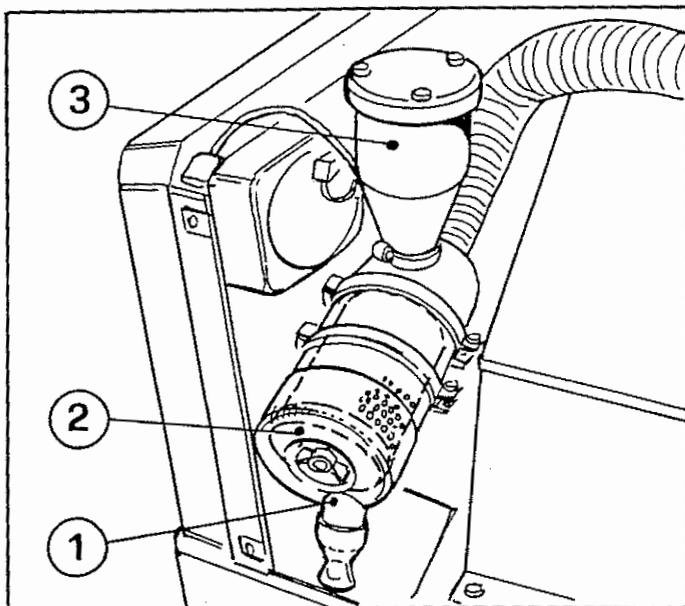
Filtro aria motore e silenziatore di aspirazione
